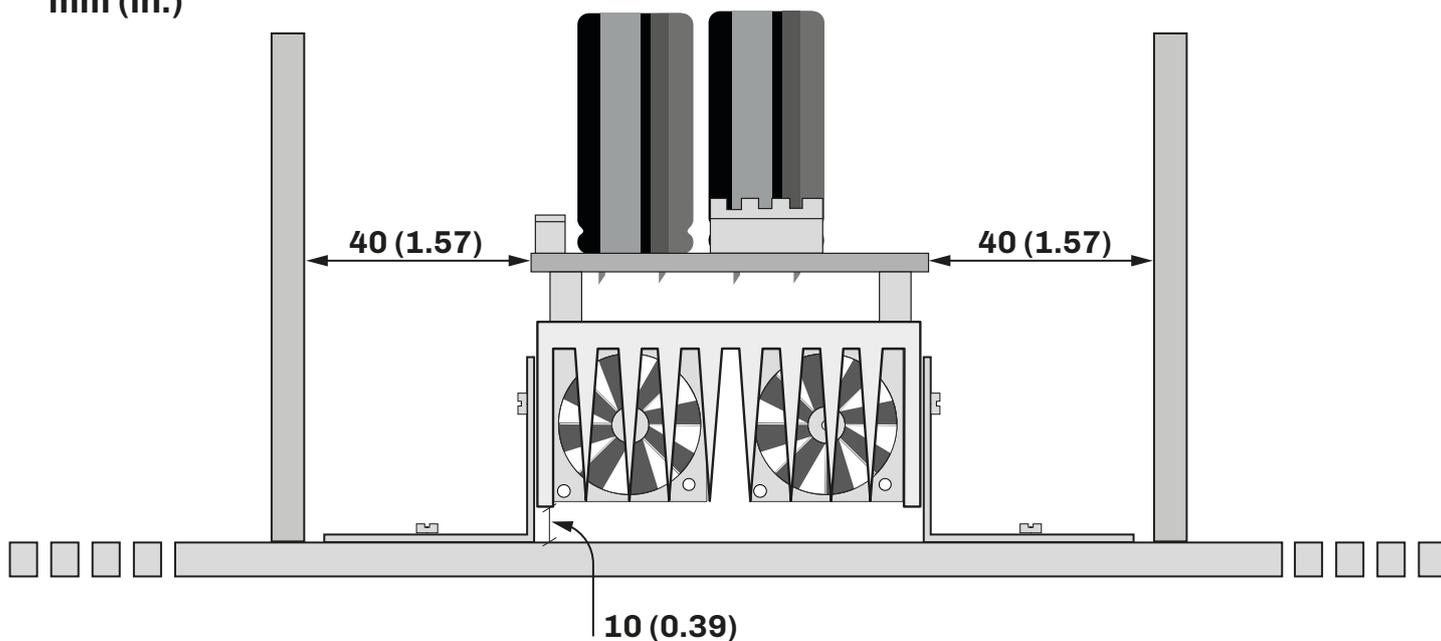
Distanze minime di montaggio Inverter - vista frontale
